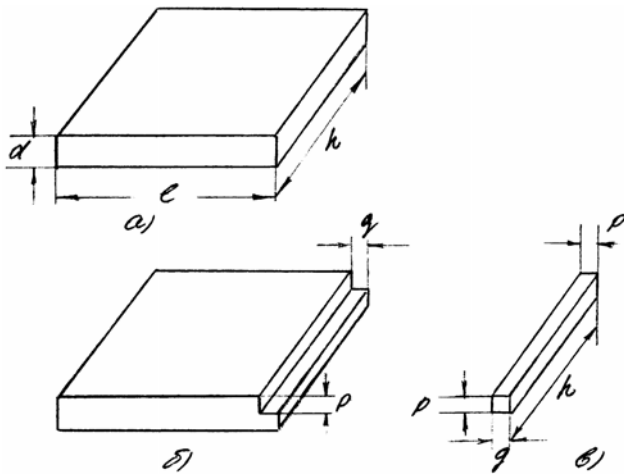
Образцовые пластины, из которых изготавливаются образцы
